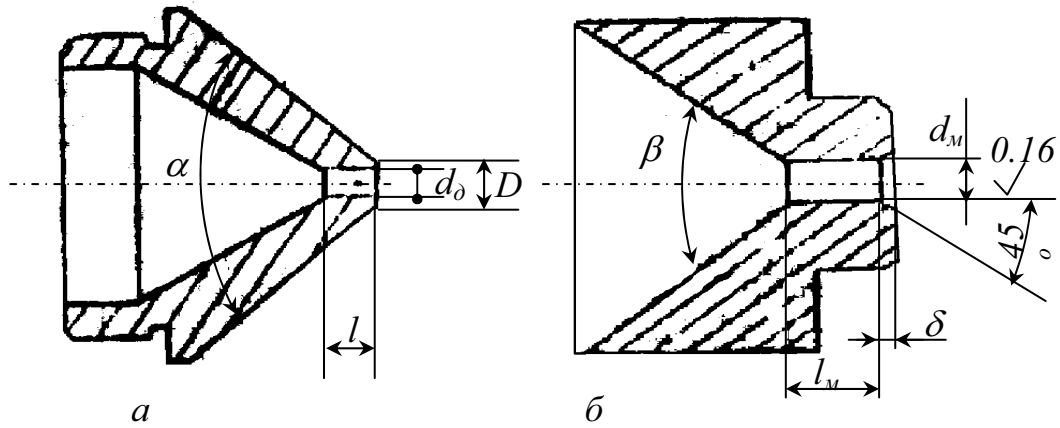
Формующий инструмент для однослойного наложения изоляции и оболочки: а – дорн; б – матрица
